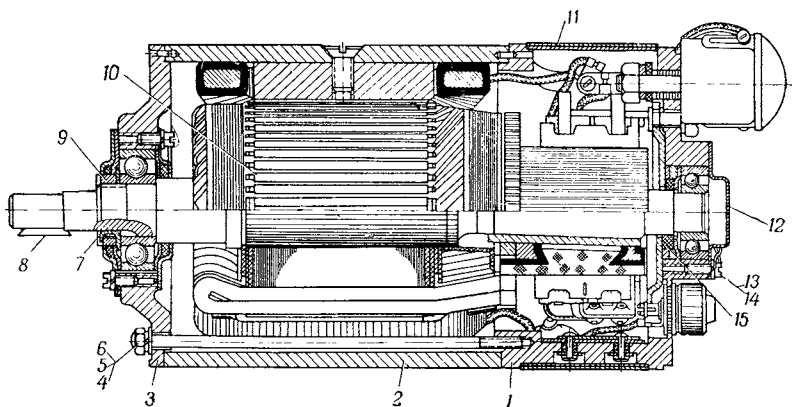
Мотор поворота башни МПБ-54 (в разрезе):
